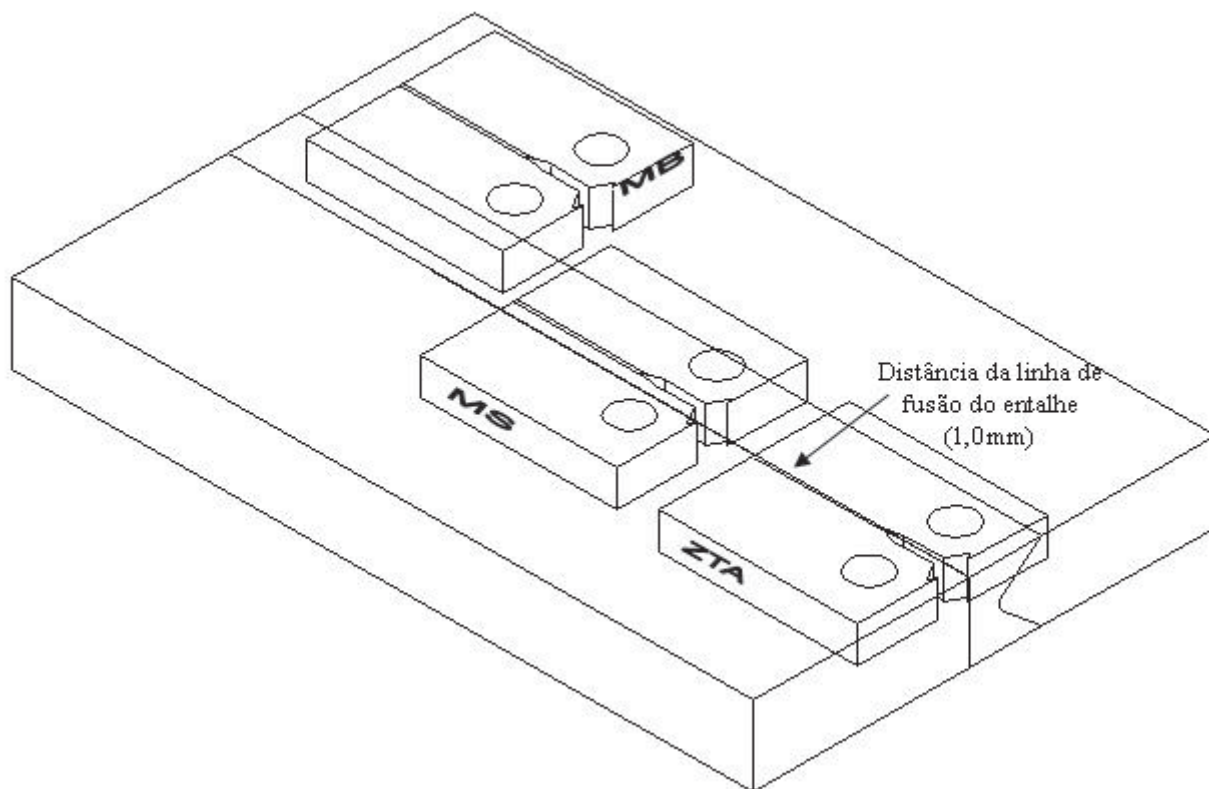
Disposição dos corpos de prova em uma junta soldada.
